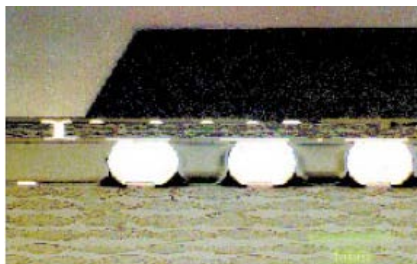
波峰焊对 PCB 上表面再流焊点的影响
